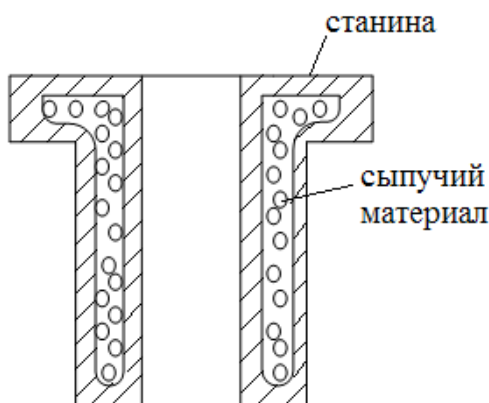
Эскиз сечения станины с сыпучим наполнителем
